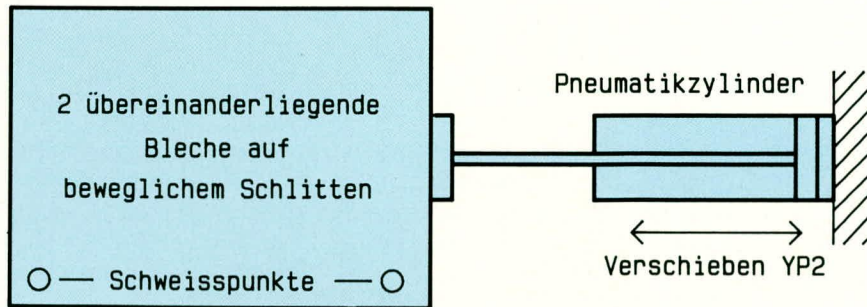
Technologieschema der Zweipunkt-Schweißvorrichtung
